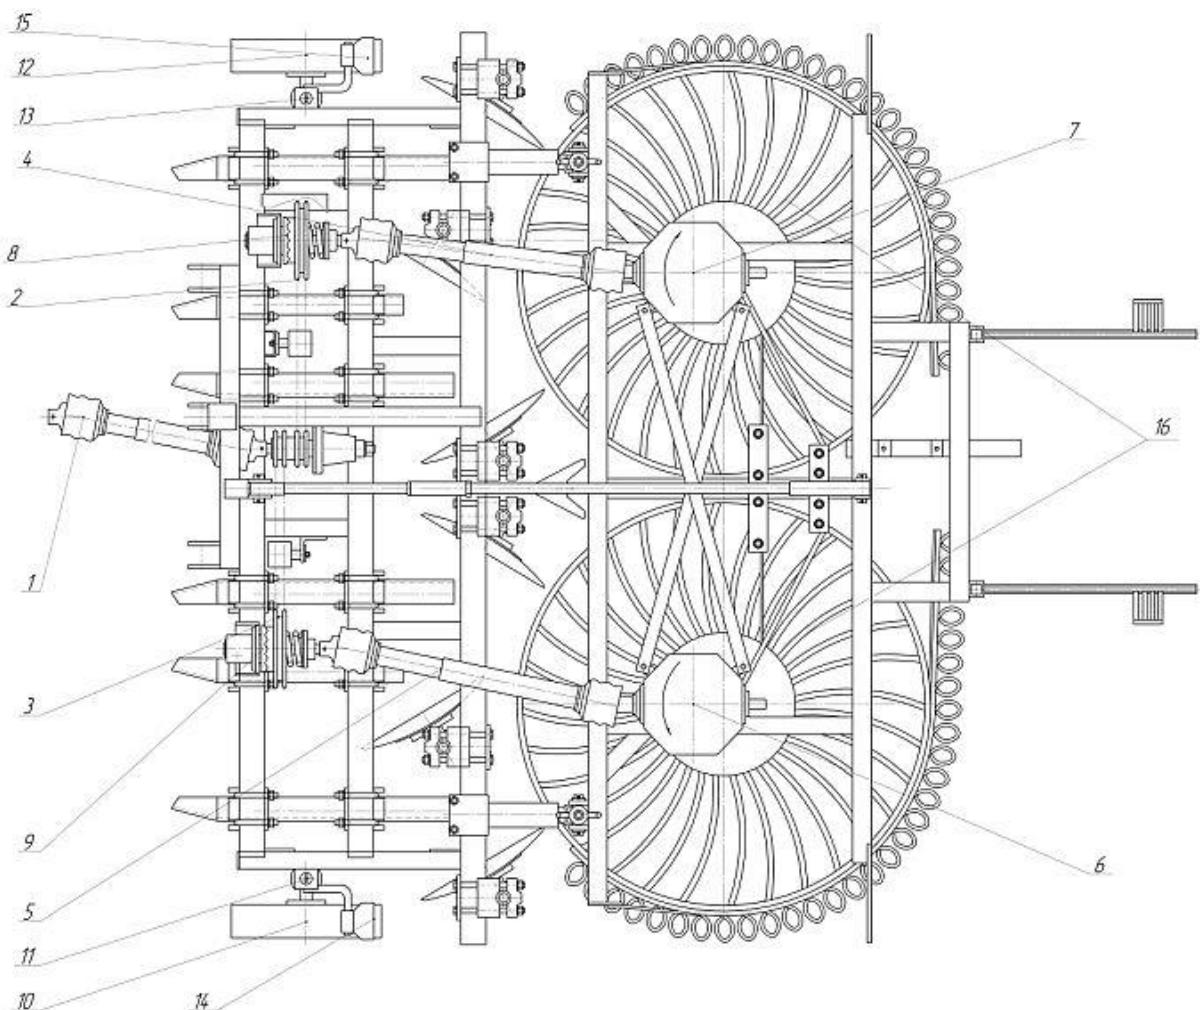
Схематичне зображення бурякозбирального агрегату АЗБ-6 (вигляд зверху): 1 – карданний вал; 2, 3 – ланцюгові передачі; 4, 5 – карданні вали приводу турбін; 6, 7 – конічні редуктори; 8, 9 – запобіжні муфти; 10, 12 – опорні колеса; 11, 13 – гвинтові механізми регулювання вертикального положення коліс; 14, 15 – чистики; 16 – турбінні колеса
